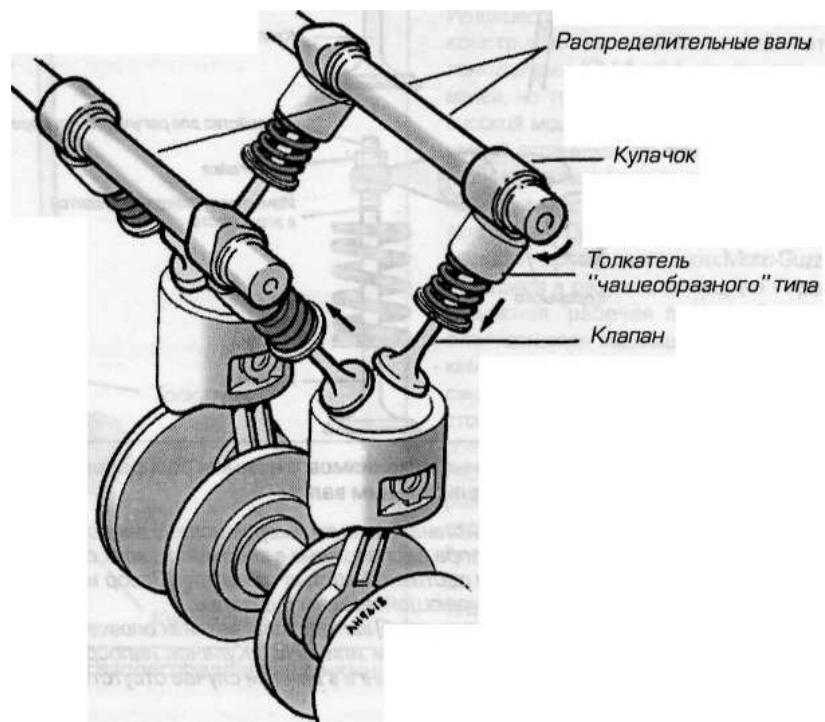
е Типичная конструкция механизма газораспределения с двумя верхними распределительными валами
